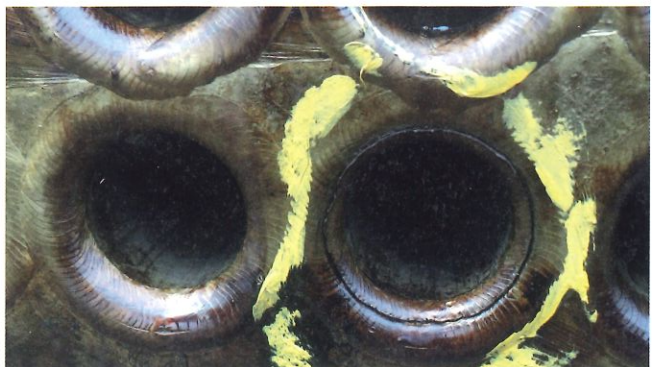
Beispiel Wärmetauscher – Detail einer durchgerissenen Einschweißung aus Bild 1
